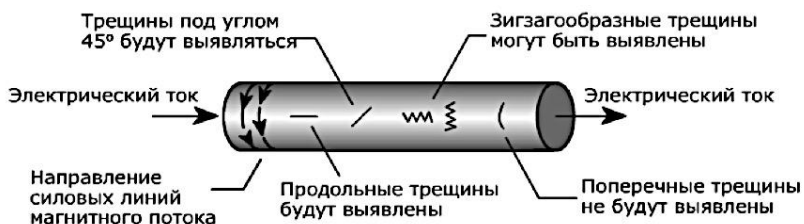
Схема намагничивания цилиндрической детали путём пропускания по ней тока [22]
